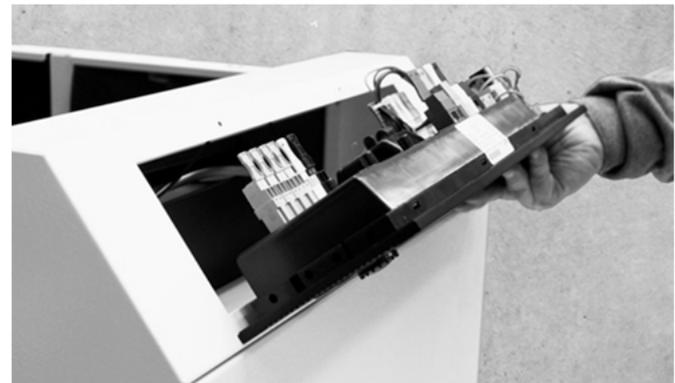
Ausgeklapptes Unit-Schaltfeld
